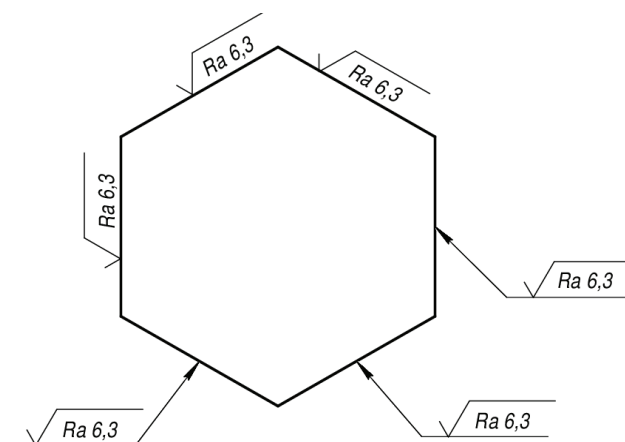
Нанесение шероховатости поверхности на линиях контура детали и на полках линий-выносок
